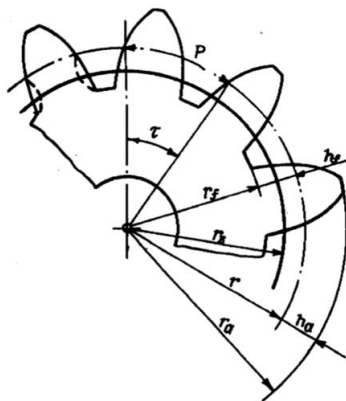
Торцовое сечение цилиндрического зубчатого колеса
